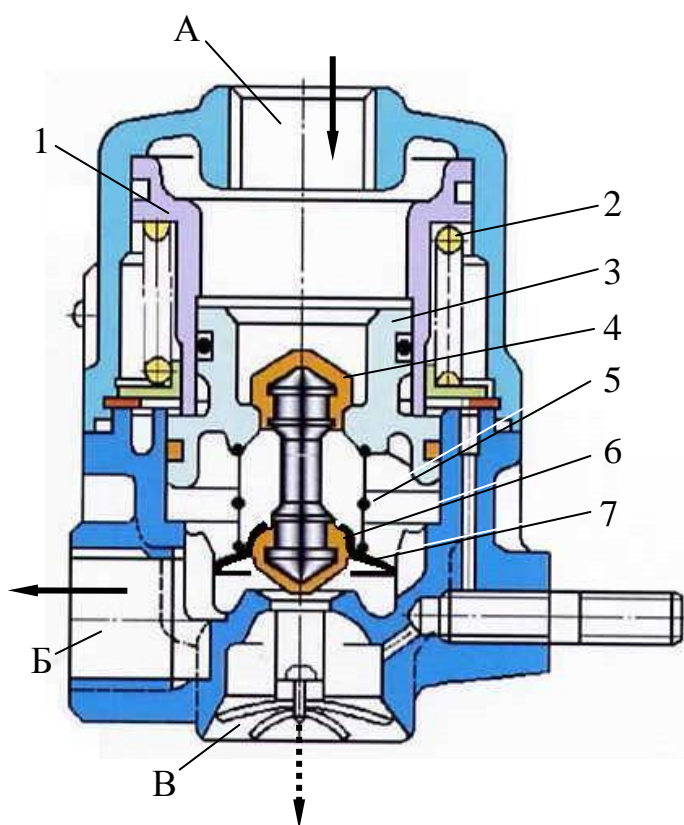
Клапан ограничения давления контура № 1 тормозного привода грузового автомобиля-тягача КАМАЗ: 1 – большой поршень; 2 – пружина; 3 – ступенчатый поршень; 4 – впускной клапан; 5 – пружина клапанов; 6 – выпускной клапан; 7 – опорная чашка; А – вывод от нижней секции двухсекционного тормозного крана; Б – вывод к тормозным камерам передних колес; В – вывод в атмосферу
